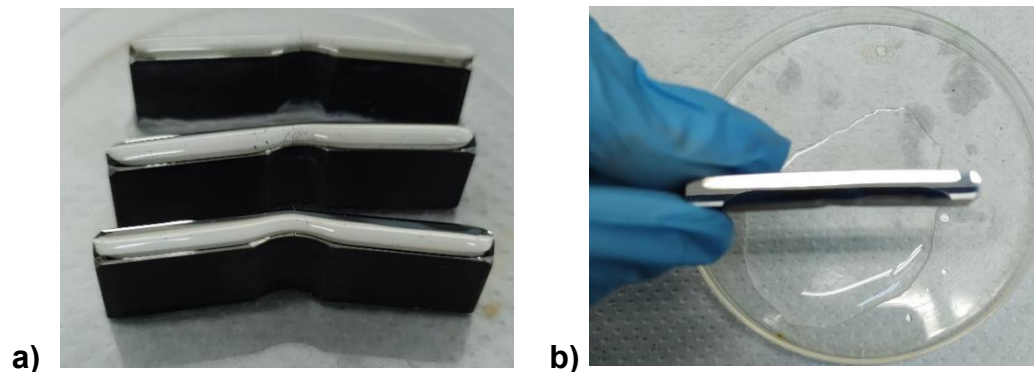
Ataque químico de las probetas: a) Soldaduras homogéneas; b) Soldadura heterogénea.
